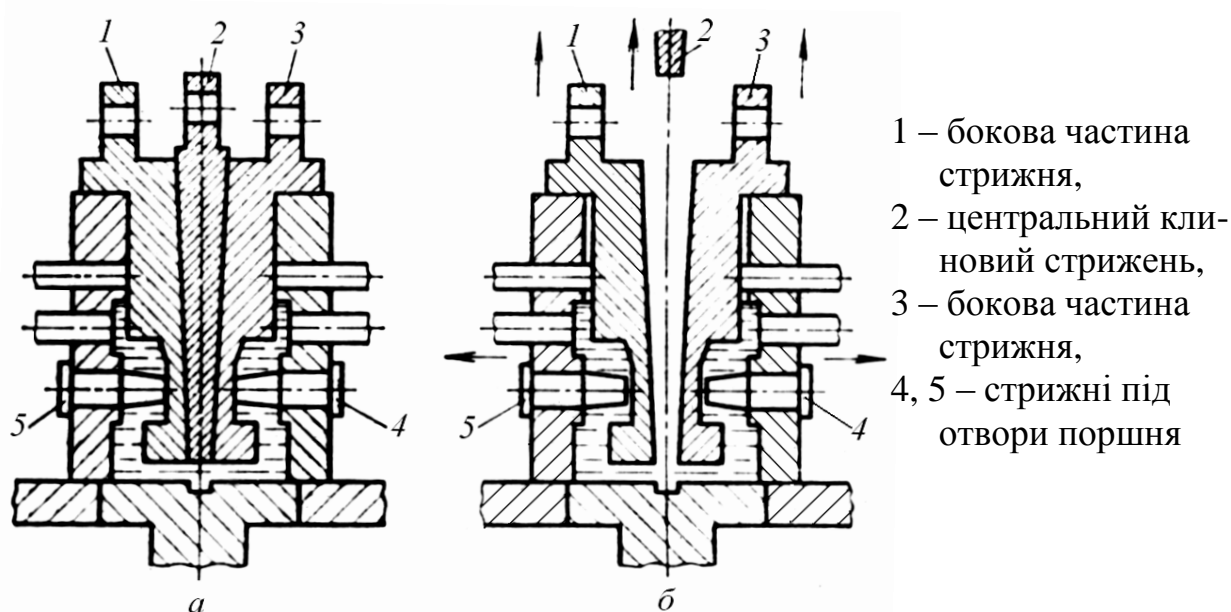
Кокіль для виливки поршня з рознімним металевим стрижнем:
